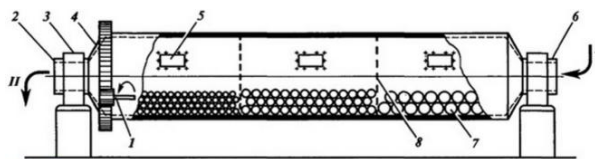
Шаровая мельница: 1 — зубчатый привод; 2 — разгрузочная полая цапфа; 3 — подшипник; 4 — барабан; 5 — люк; 6 — загрузочная полая цапфа; 7 — дробящие тела; 8 — перегородка
